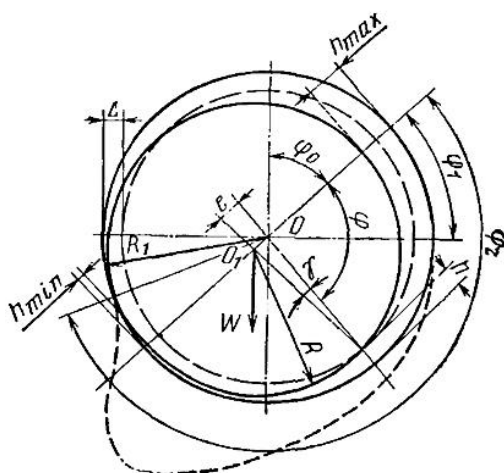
Схема подшипника с цилиндрической расточкой
